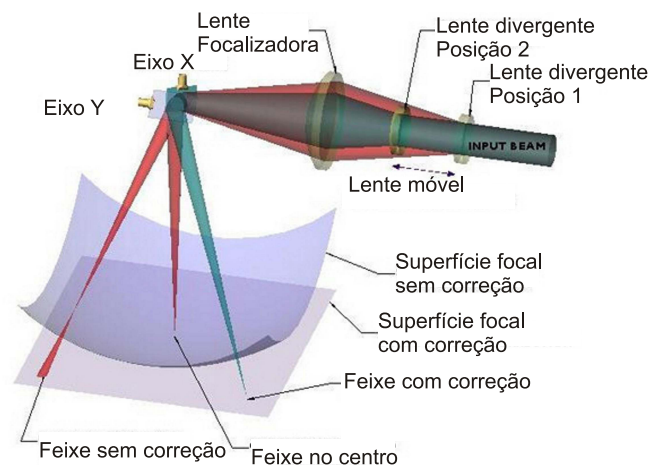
Princípio de operação de máquina galvanométrica com 3 eixos
